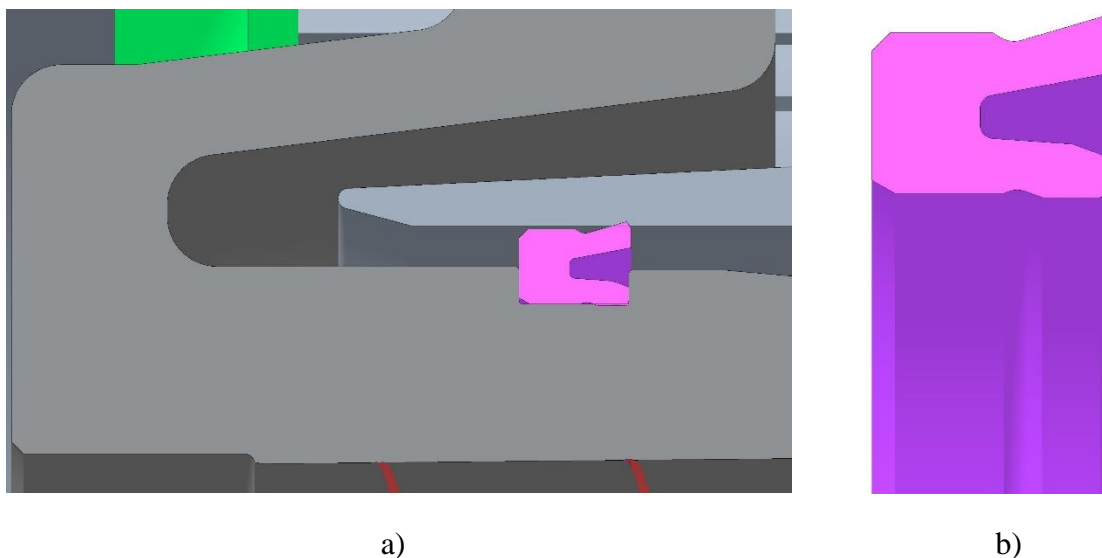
Model středového kroužku: a) obecný pohled, b) zobrazení v řezu
